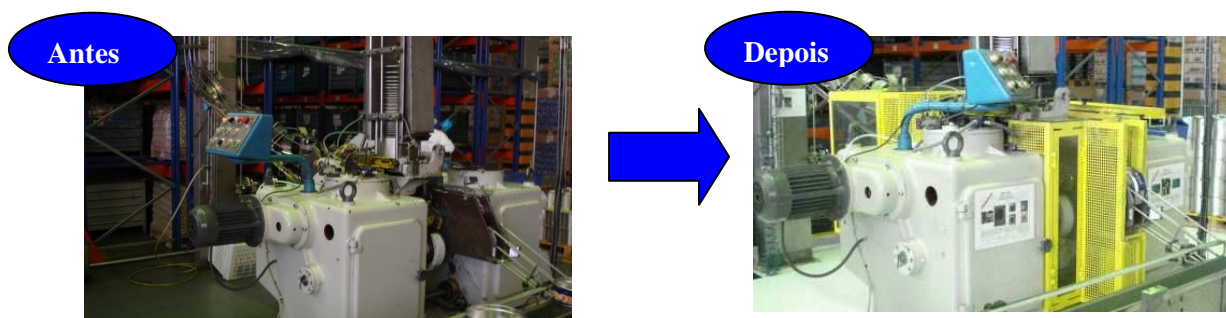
Aplicação da protecção na cravadeira da linha 22
